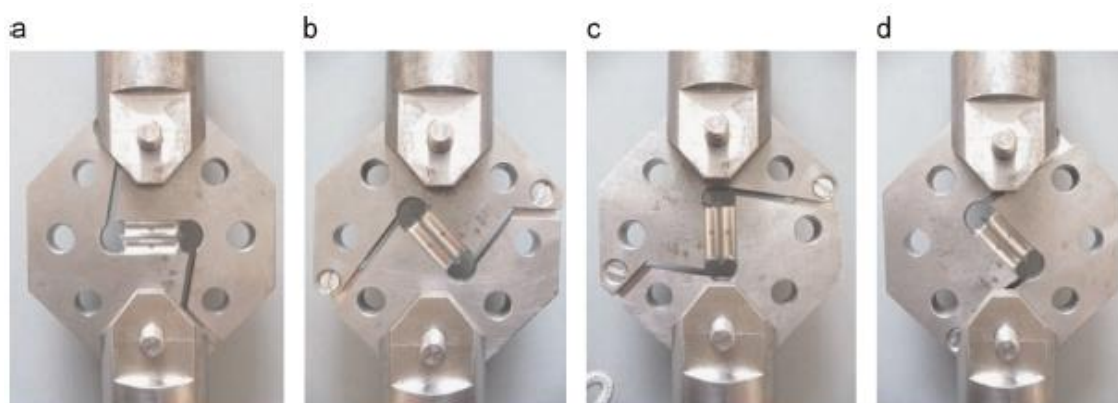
Configurações do ensaio a) tração; c) cisalhamento; b) e d) tração + cisalhamento
